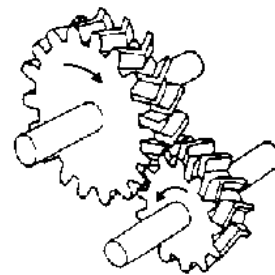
Engranatge amb rodes tallades en "dent de fletxa"
